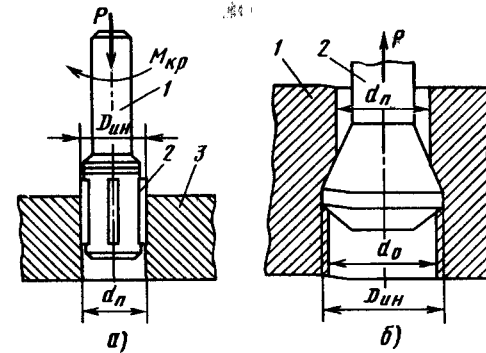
Упрочнение отверстий путем пластической деформации отверстий: а — схема раскатывания отверстия: 1 — регулируемая оправка; 2 — конические ролики; 3 — упрочняемая деталь; б — схема дорнирования отверстия: 1 — обрабатываемая деталь; 2 — дорн; Р — усилие подачи;  $M_{кр}$  — крутящий момент, создаваемый инструментом;  $D_{ин}$  — диаметр инструмента;  $d_{п}$  — диаметр предварительной разделки отверстия;  $d_{о}$  — диаметр отверстия после обработки
